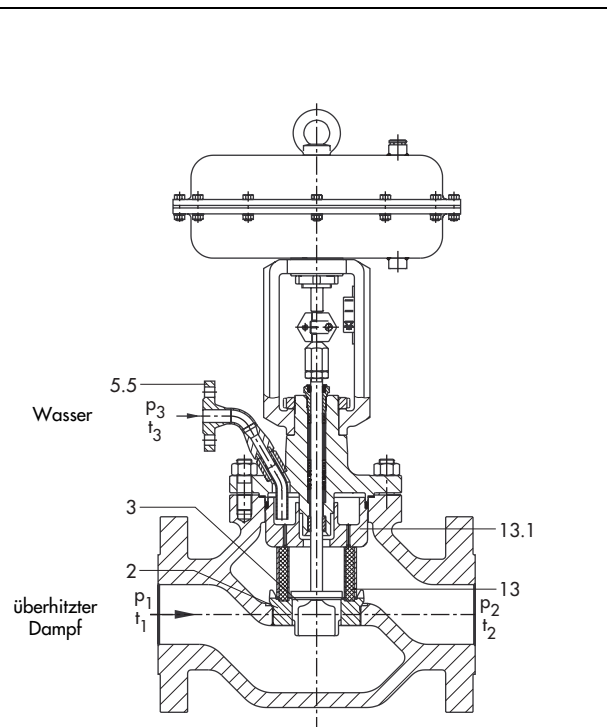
· Pneumatischer Dampfumformer Typ 3281-1 mit Flanschanschluss und Antrieb Typ 3271
